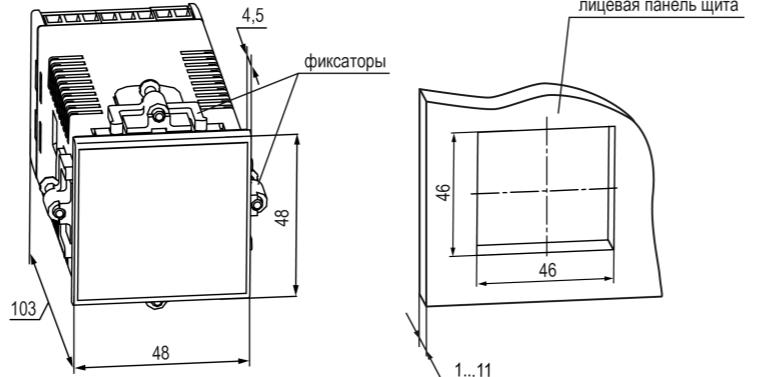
Габаритные размеры корпуса Щ5 и монтажного отверстия в щите
